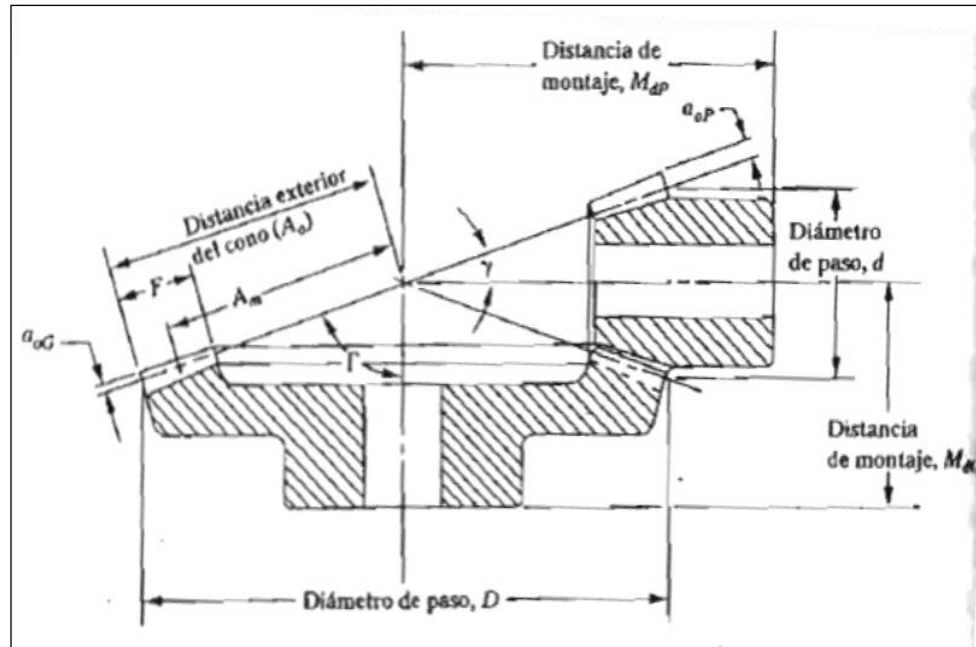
Dimensiones principales de un par de engranajes cónicos con dientes rectos⁵⁰
